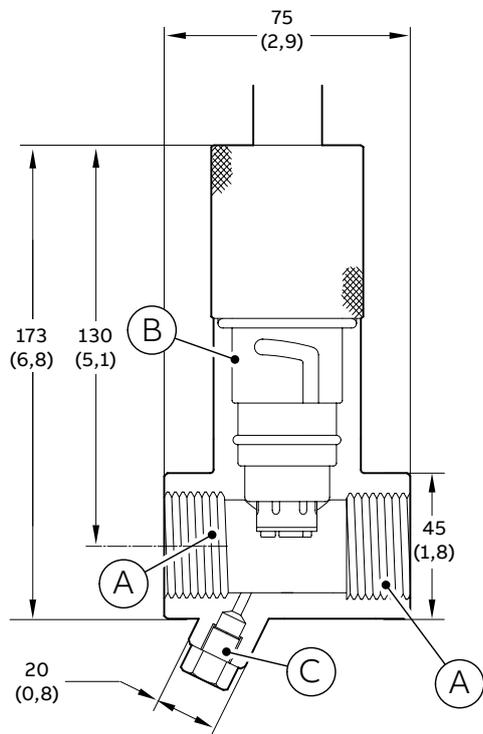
Тройник со штифтовым креплением — резьба NPT
